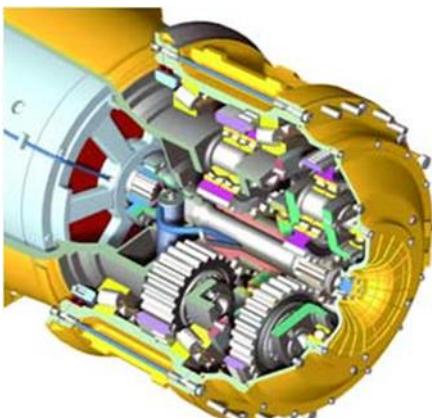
Редуктор мотор-колеса (PMK) самосвала
